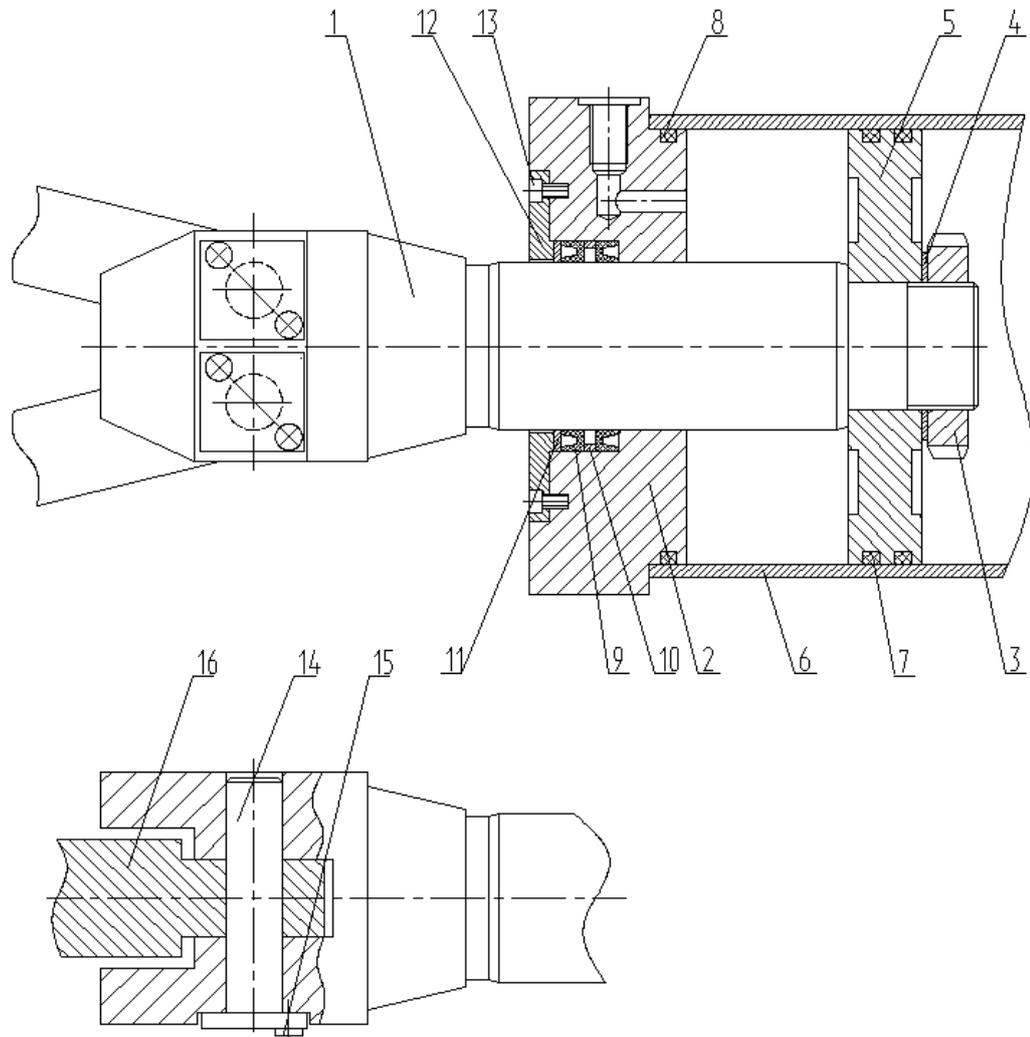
Фрагмент механизма узла привода пресс-ножниц
